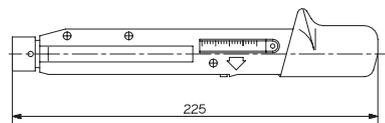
Drehmomentschlüssel Typen 1300A11 und 1300A39
